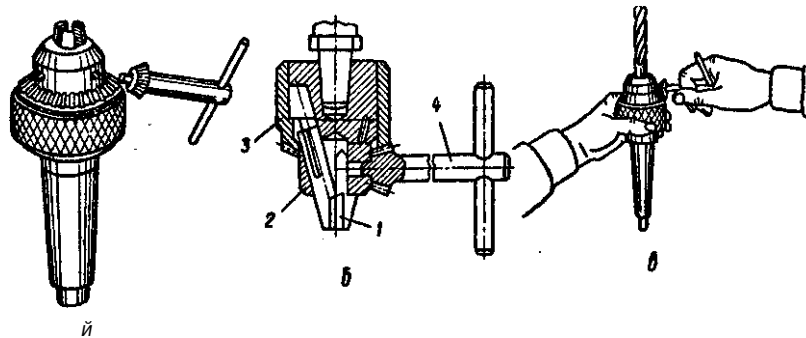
Трикулачковий свердильний патрон для кріплення свердел з циліндричним хвостовиком (*a* і *б*) і кріплення свердла (*в*)
